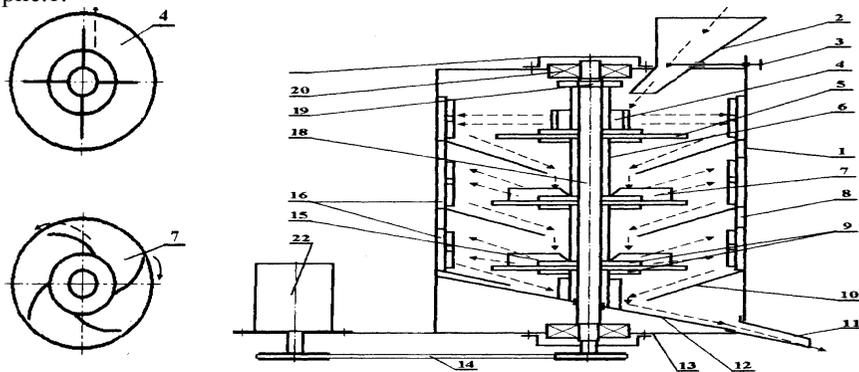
Схема устройства скарификатора семян бобовых трав: 1 – корпус; 2 – засыпная горловина; 3 – задвижка регулировки потока семян; 4 – крыльчатка прямая, крестообразная для равномерного распределения семян; 5 – диск наждачный; 6 – распорная втулка; 7 – крыльчатка изогнутая для скольжения семян; 8 – распорная втулка распределителей семян; 9 – фланцы; 10 – распределитель семян; 11 – съемный лоток; 12 – скатывающий лоток; 13 – основание; 14 – ременная передача; 15 – направляющие канавки; 16 – ленты наждачные для скарификации семян; 17 – распорная втулка; 18 – вал; 19 – зажимная гайка; 20 – подшипник; 21 – крышка подшипника; 22 – электродвигатель 1000 об/мин, 2 кВт
